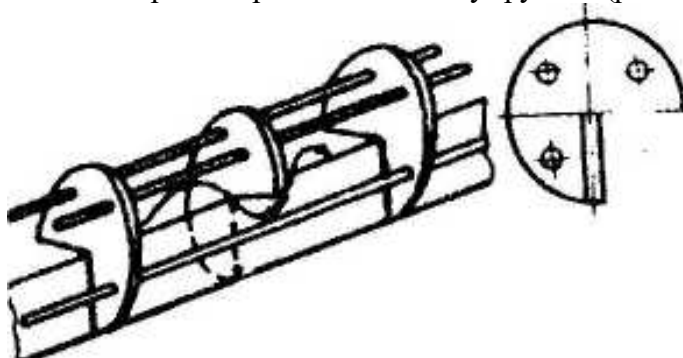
Конструктивная схема поперечных перегородок
